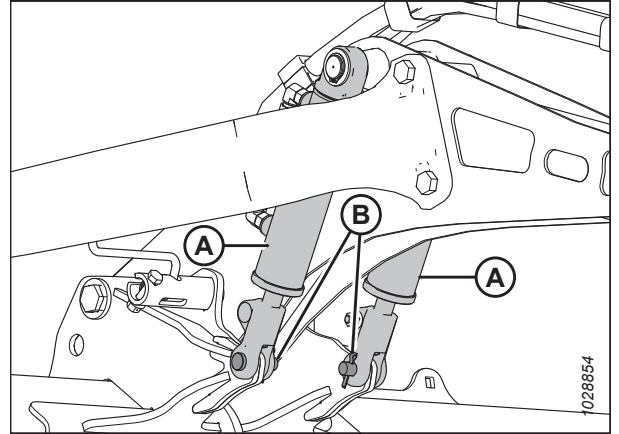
Vérins de levage au niveau du bras central du rabatteur
